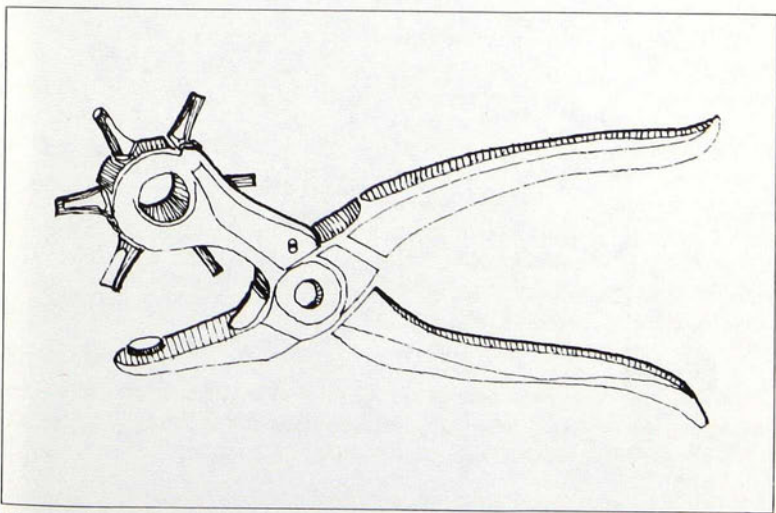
Le découpoir à l'emporte-pièce ou pince à oeillets sert à pratiquer dans le cuir des ouvertures circulaires de différentes dimensions.
